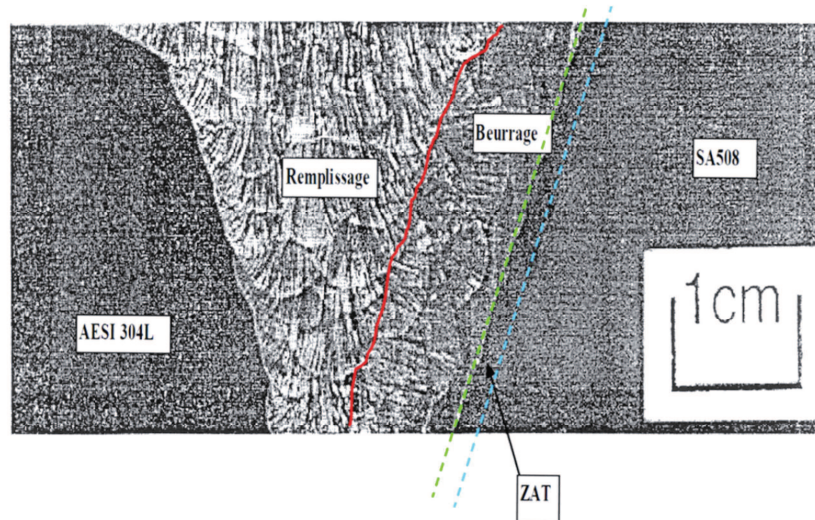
Soudure des maquettes du programme BIMET [GIL 09-1]
